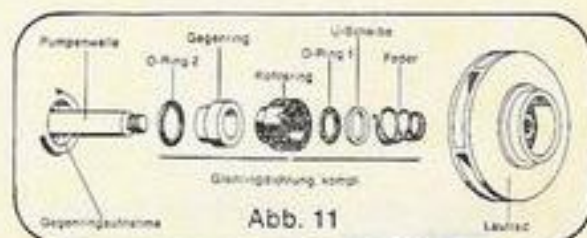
Austausch der Gleitringdichtung. Hinter dem Laufrad befindet sich die Gleitringdichtung. Zum Ausbau Feder, Unterlegscheibe, O-Ring 1 und Kohlering von der Welle abziehen.
